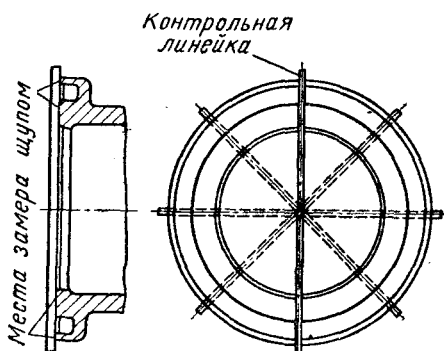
Схема проверки привалочных поверхностей рамы и цилиндра
